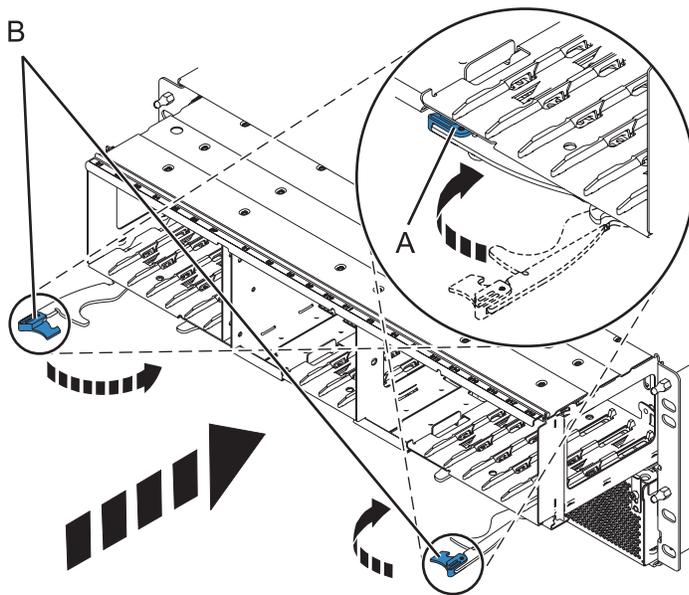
Installation du fond de panier sur un modèle monté en armoire
